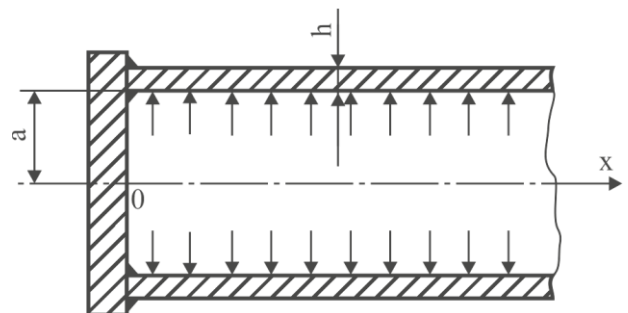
Розрахункова схема для довгої циліндричної оболонки [45]
